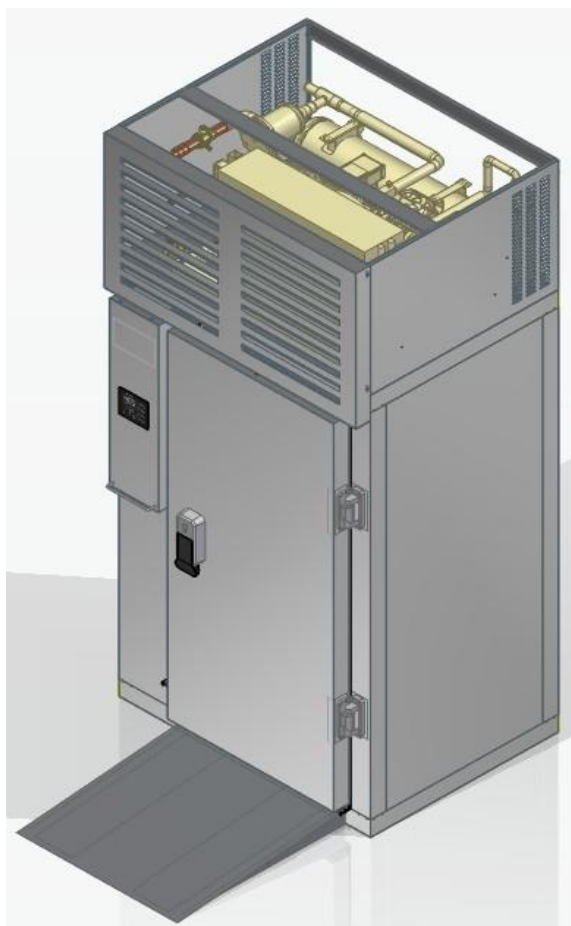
Внешний вид камеры ШОКК-20Т-К
